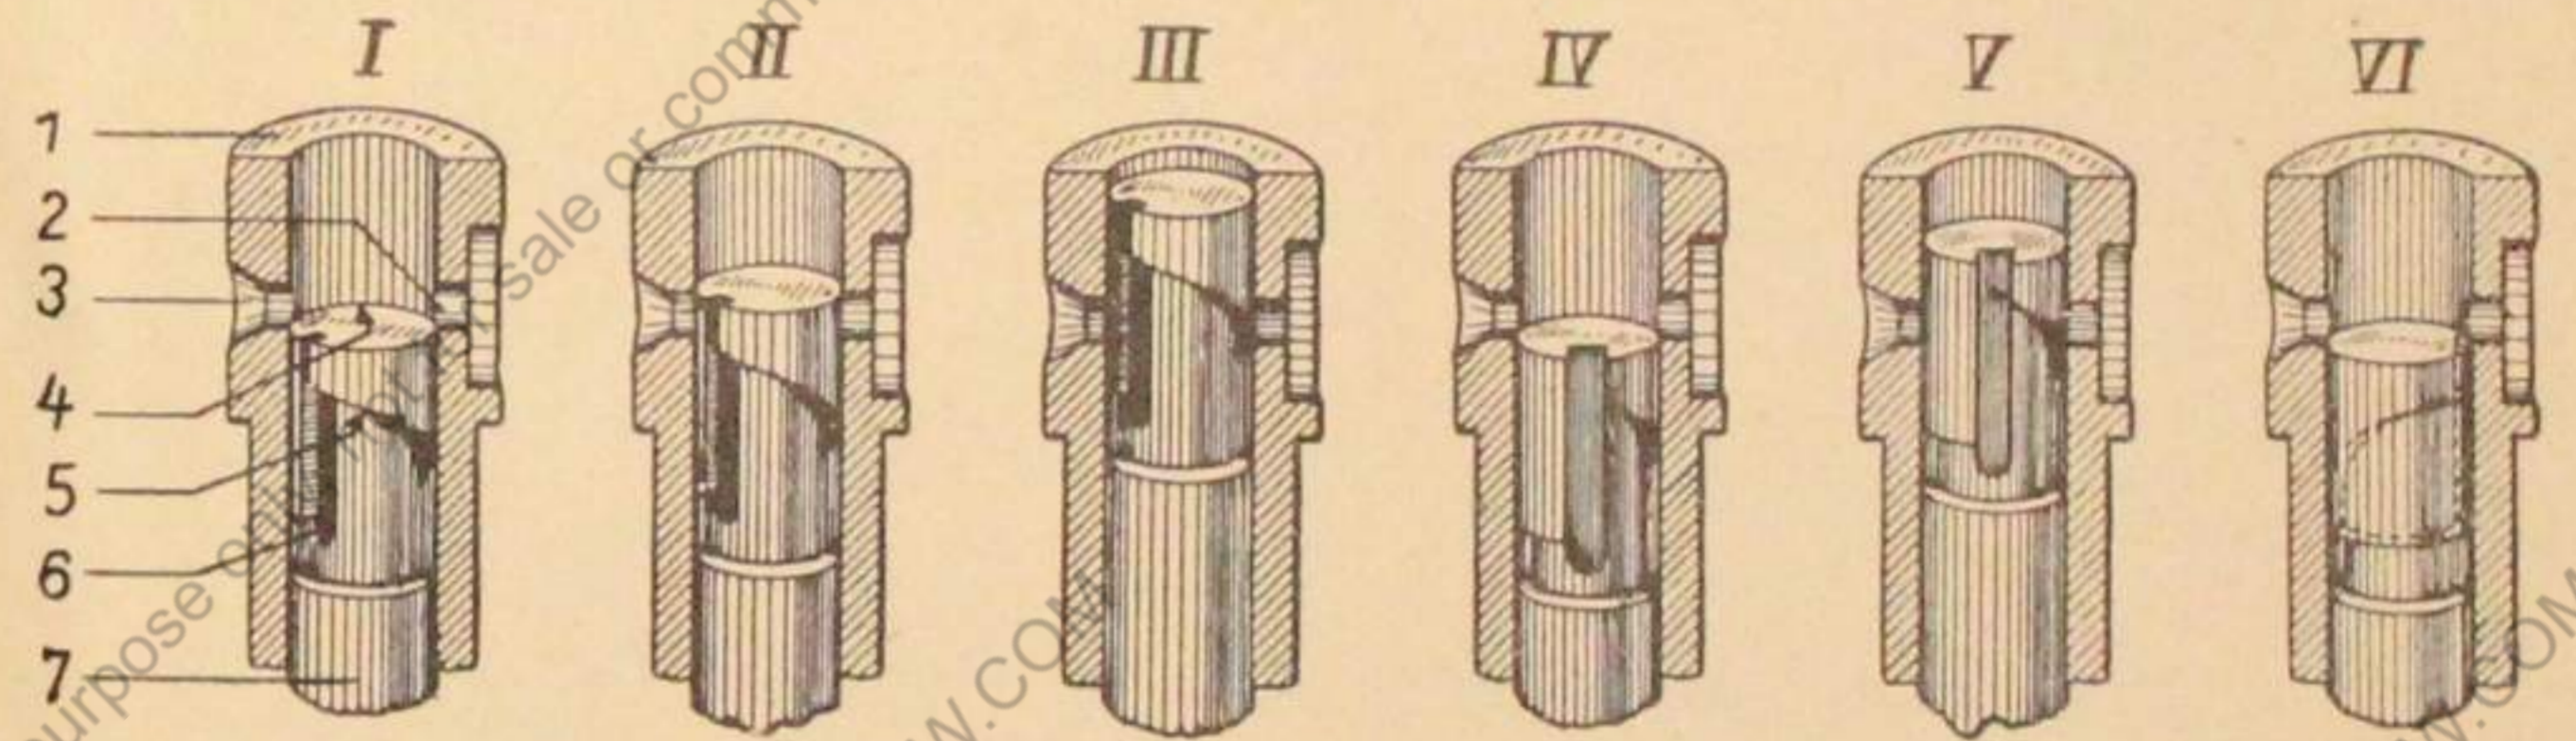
Wirkungsweise der Bosch-Einspritzpumpe
